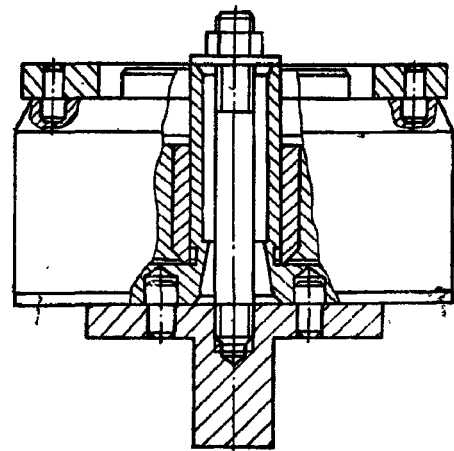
Установка муфты опережения впрыска топлива в приспособление И801.16.000 для разборки-сборки
